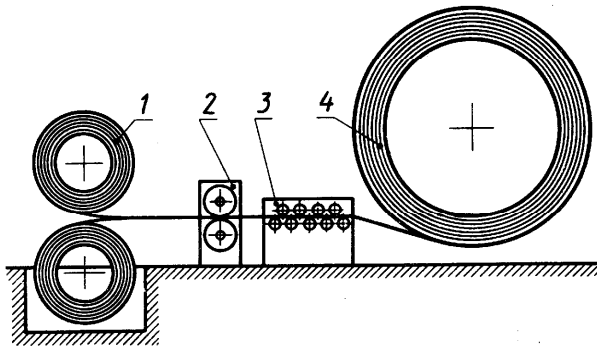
Схема процесса изготовления плоскосвариваемых труб
